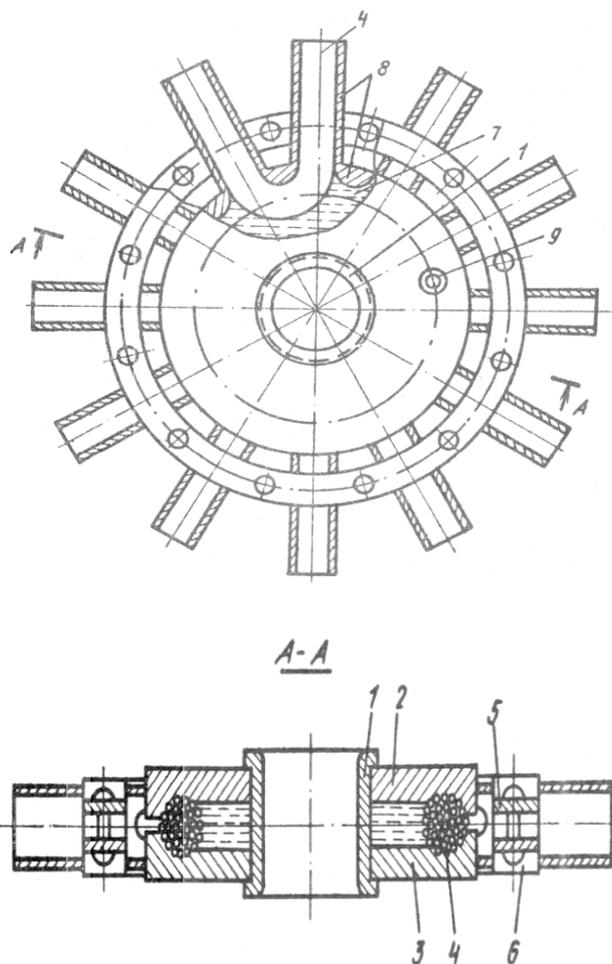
Схема радиальной щетки цилиндрической формы с U-образными пучками ворсовых элементов и кольцевой камерой для пластичного смазочного материала
